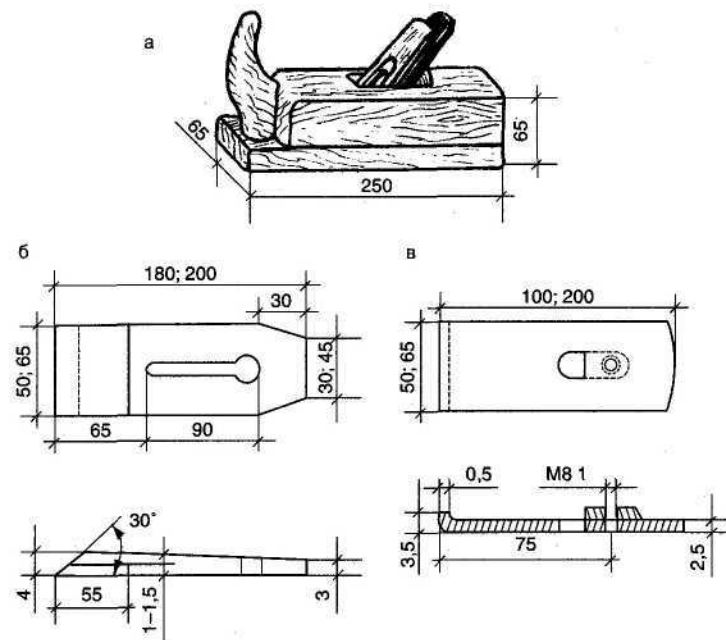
Рубанок с двойным ножом (размеры в мм):
